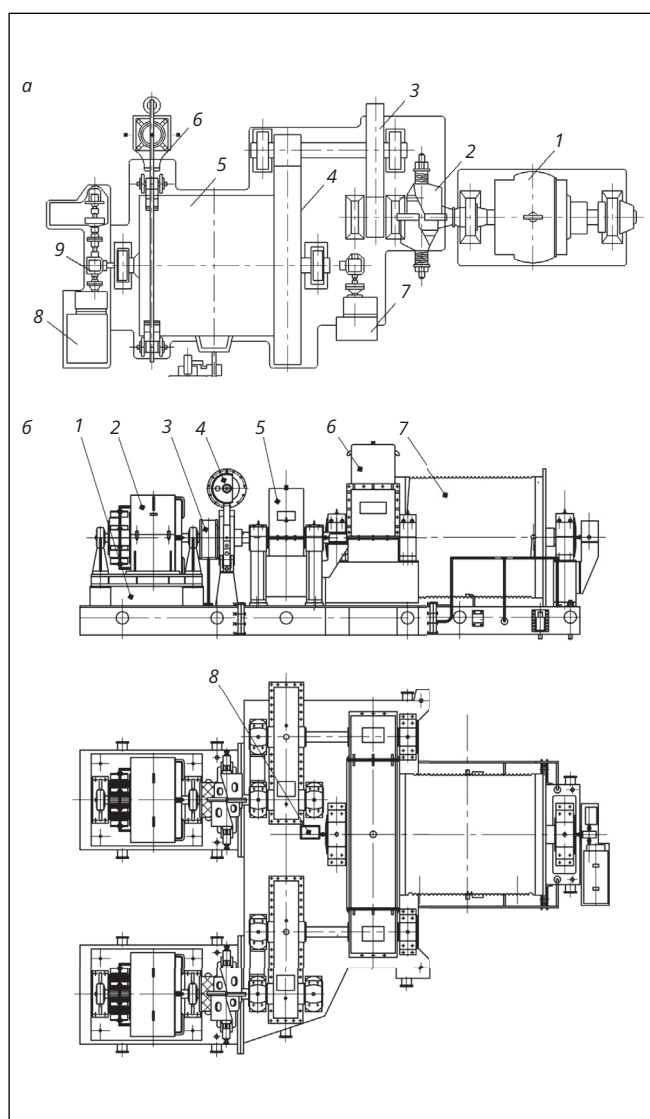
Сравнение схем расположения элементов скиповых лебедок фирмы «Отис» (а: 1 — электродвигатель; 2 — рабочий тормоз; 3 — быстроходный и 4 — тихоходный редукторы; 5 — барабан; 6 — аварийный тормоз; 7 — 9 — выключатели; 7 — аварийный, 8 — рабочий, 9 — центробежный) и модели ЛС-39-1 (б: 1 — станина; 2 — электродвигатель; 3 — зубчатая муфта; 4 — тормоз; 5 — быстроходный и 6 — тихоходный редукторы; 7 — барабан; 8 — командоаппарат)
